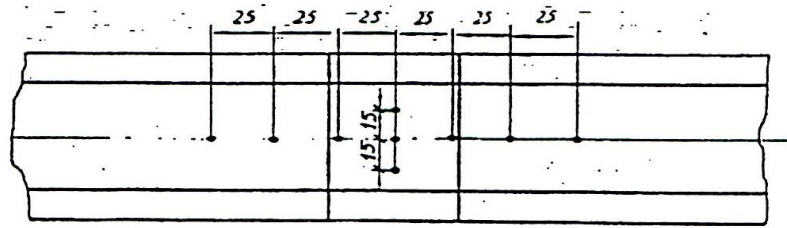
Схема измерения твёрдости сварного соединения
